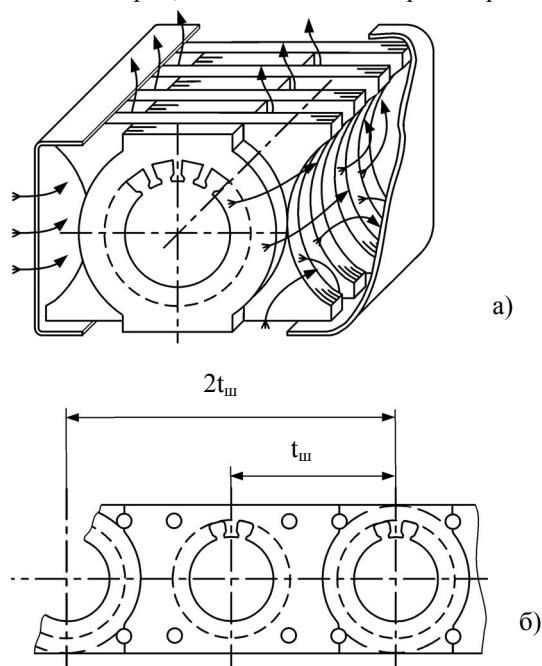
Конструктивная схема (а) и раскрой полосы (б) стали для изготовления магнитопровода бескорпусного статора с аксиально-тангенциальным охлаждением
